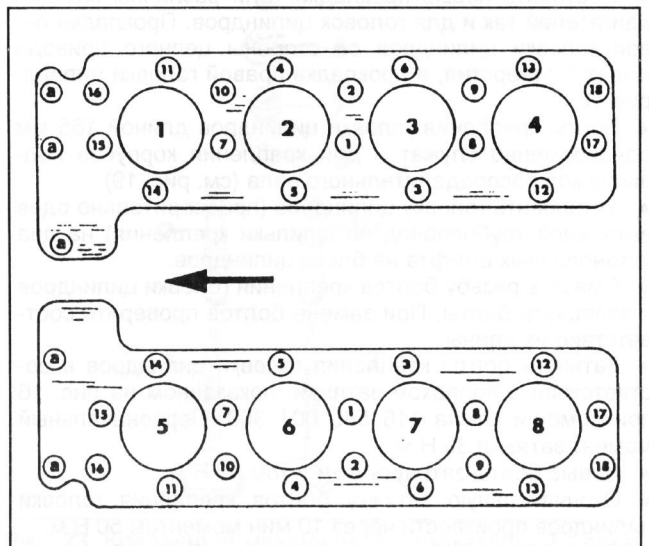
Порядок затяжки болтов крепления головки цилиндров.
